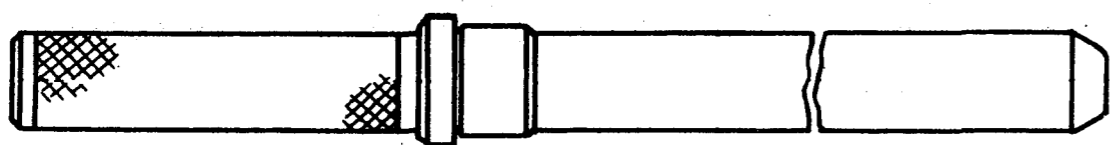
Оправка 7820-4797 для установки упорных шайб блока шестерен
